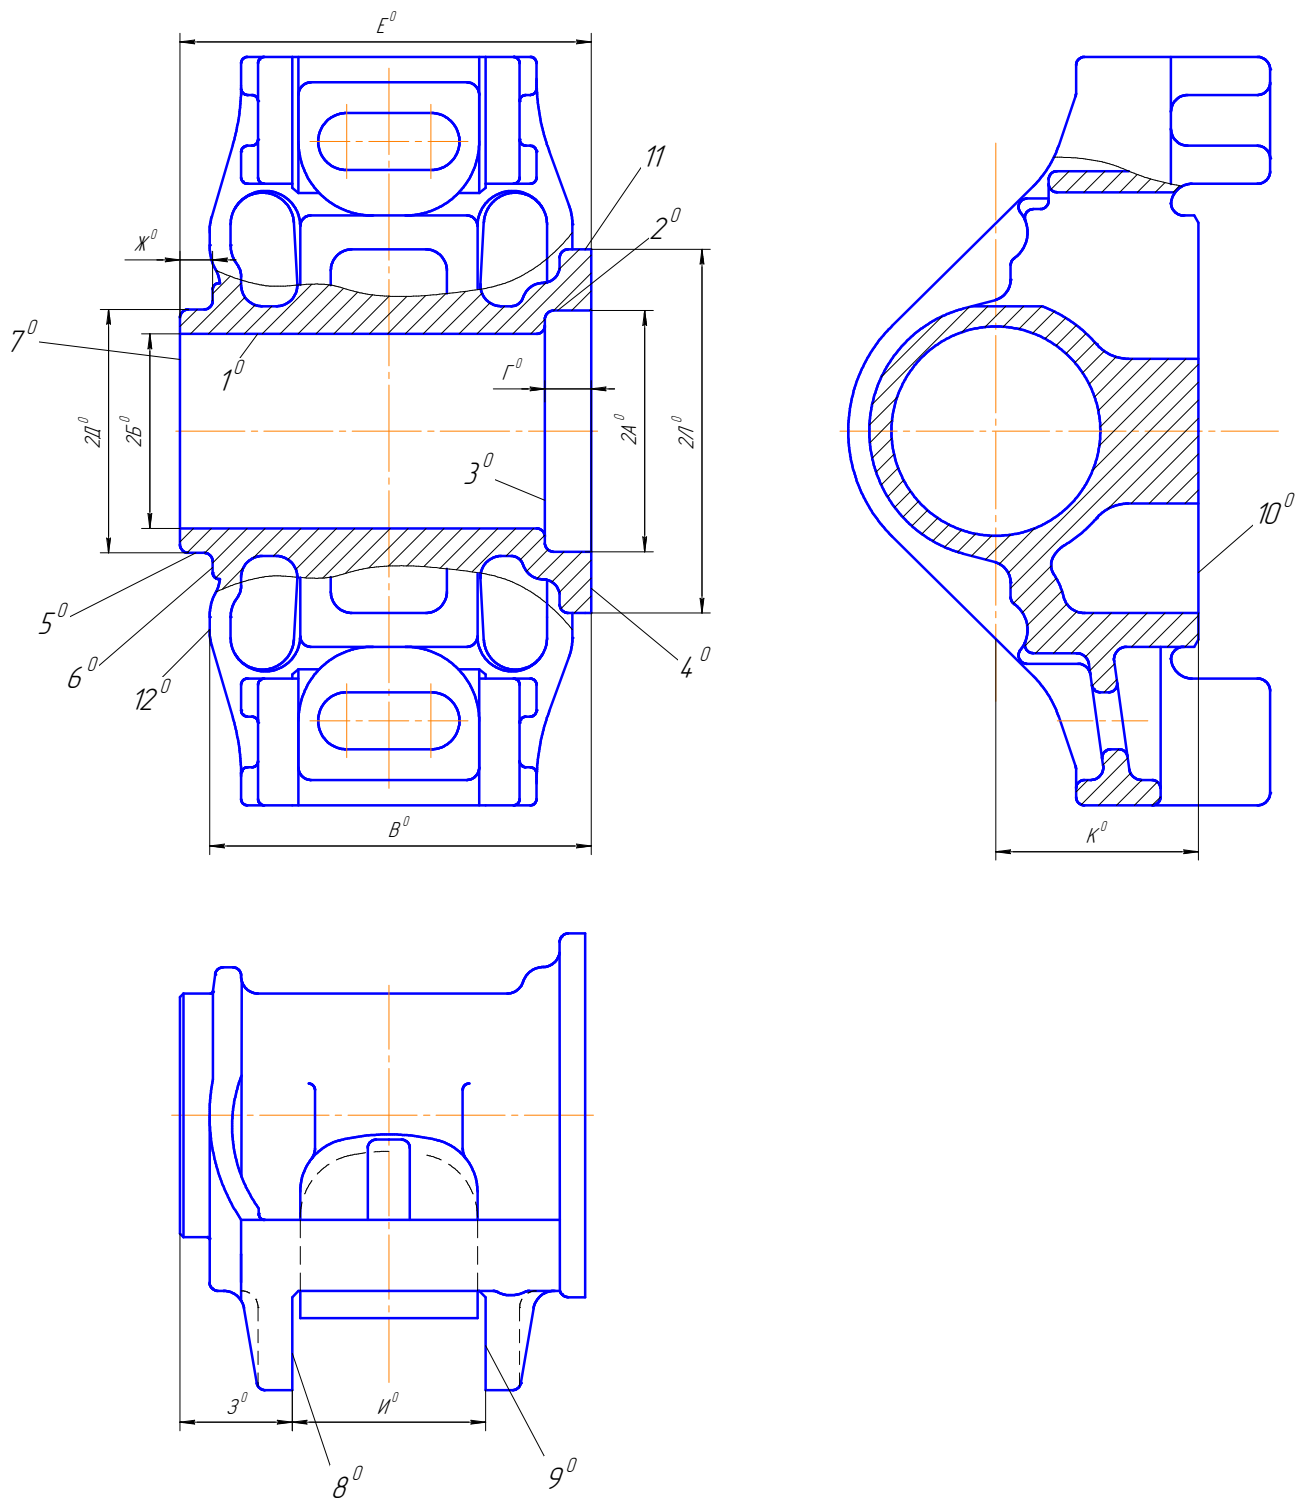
Эскиз заготовки с размерами.
